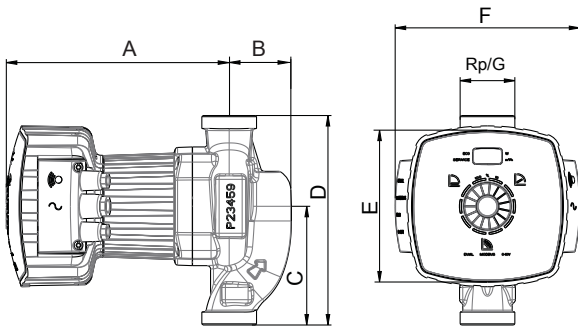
Pumpenaggregat mit Gewindeanschluss
